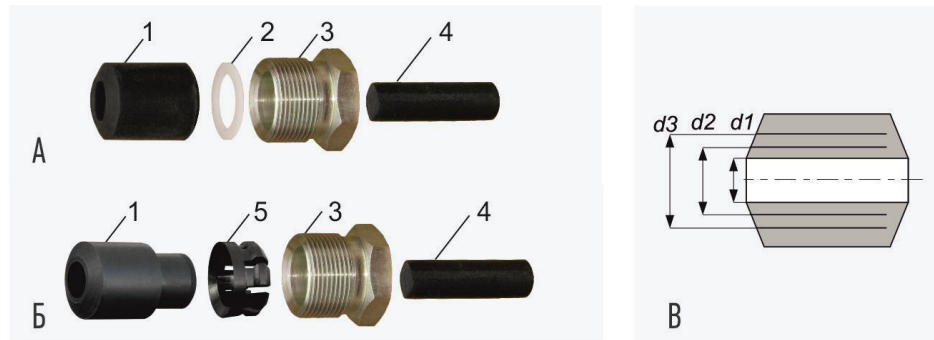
Устройство крепления металлорукава УКМ-10 (-12) для кабельного ввода "D12":
